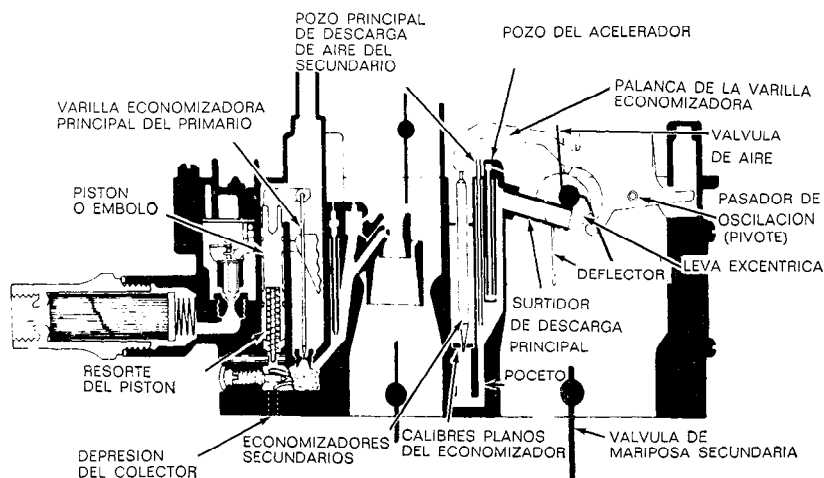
Vista en sección de un carburador con pistón de regulación del economizador, accionado por la depresión del colector de admisión (Buick Motor Division of General Motors Corporation).
